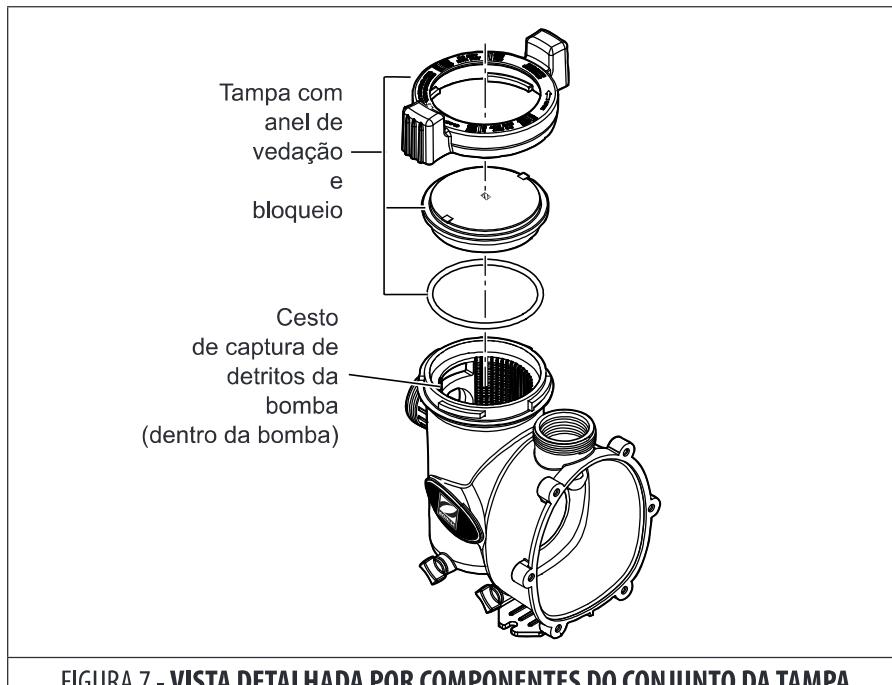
VISTA DETALHADA POR COMPONENTES DO CONJUNTO DA TAMPA
